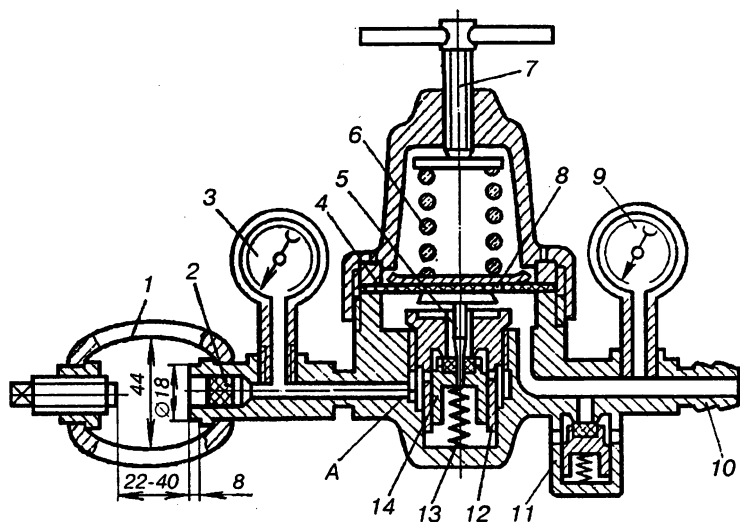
Схема ацетиленового редуктора ДАП-1-65:
